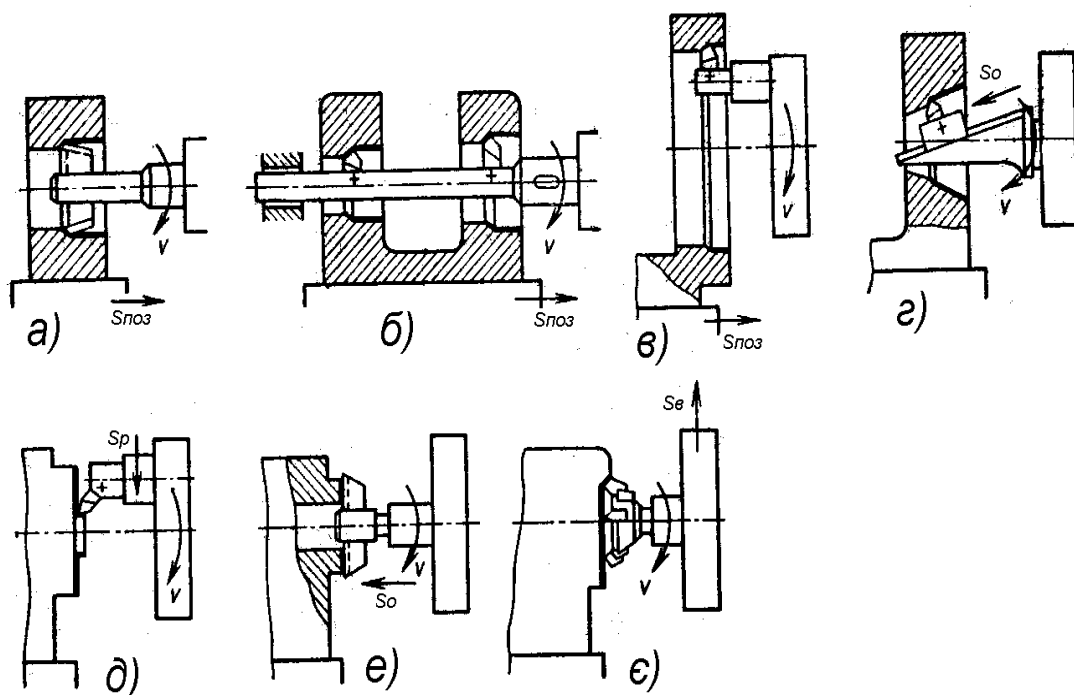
Схеми обробки заготовок на горизонтально-розточувальних верстатах
